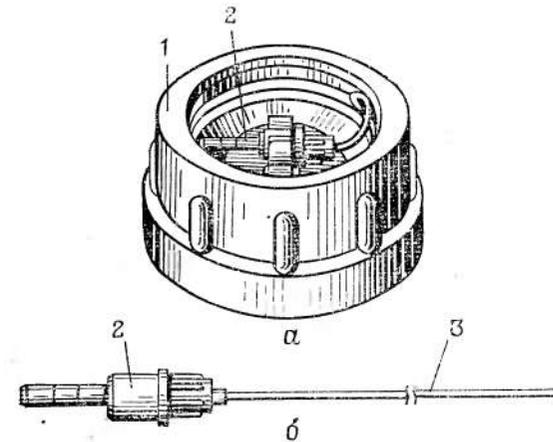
Обрывной датчик взрывателя МВЭ-72:
